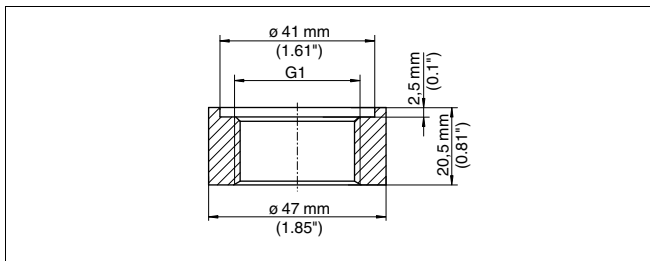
Размеры приварного штуцера G1 A по DIN 3852-X
